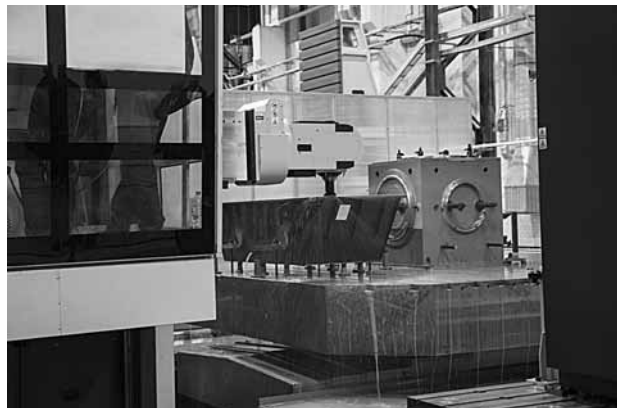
Горизонтальный расточно-фрезерный станок с ЧПУ WRD 1700, «TOS Varnsdorf», Чехия
